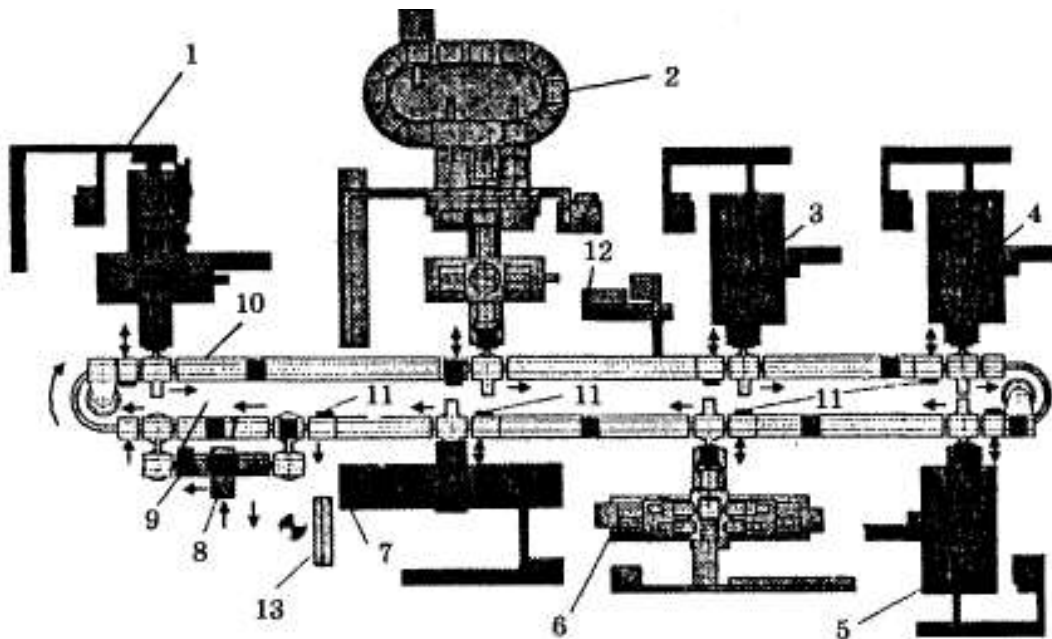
Лінія для обробки двох корпусних деталей
